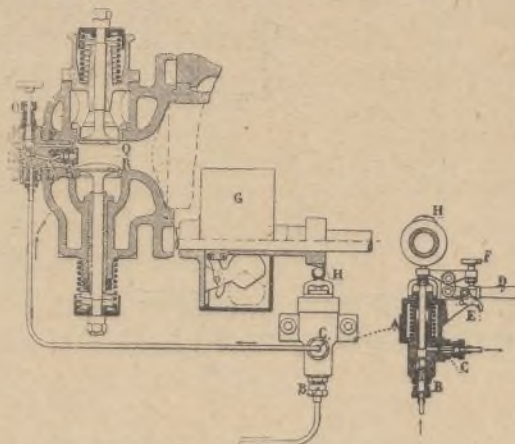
Corte esquemático de la distribución del motor sistema Dingler.
